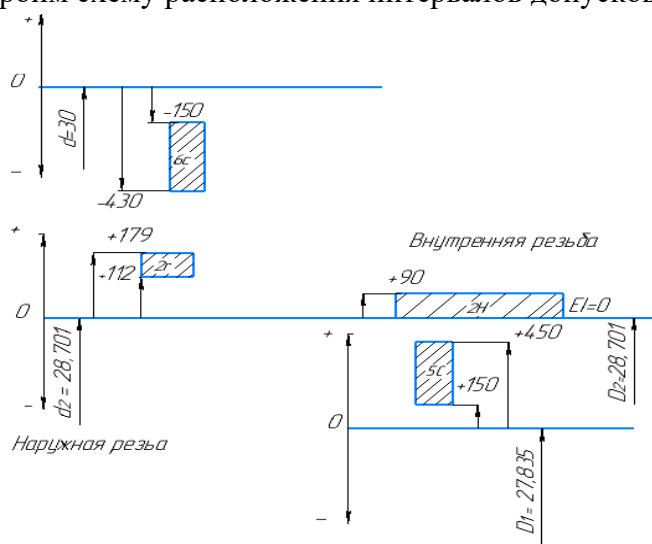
Схема полей допусков резьбового соединения с натягом
